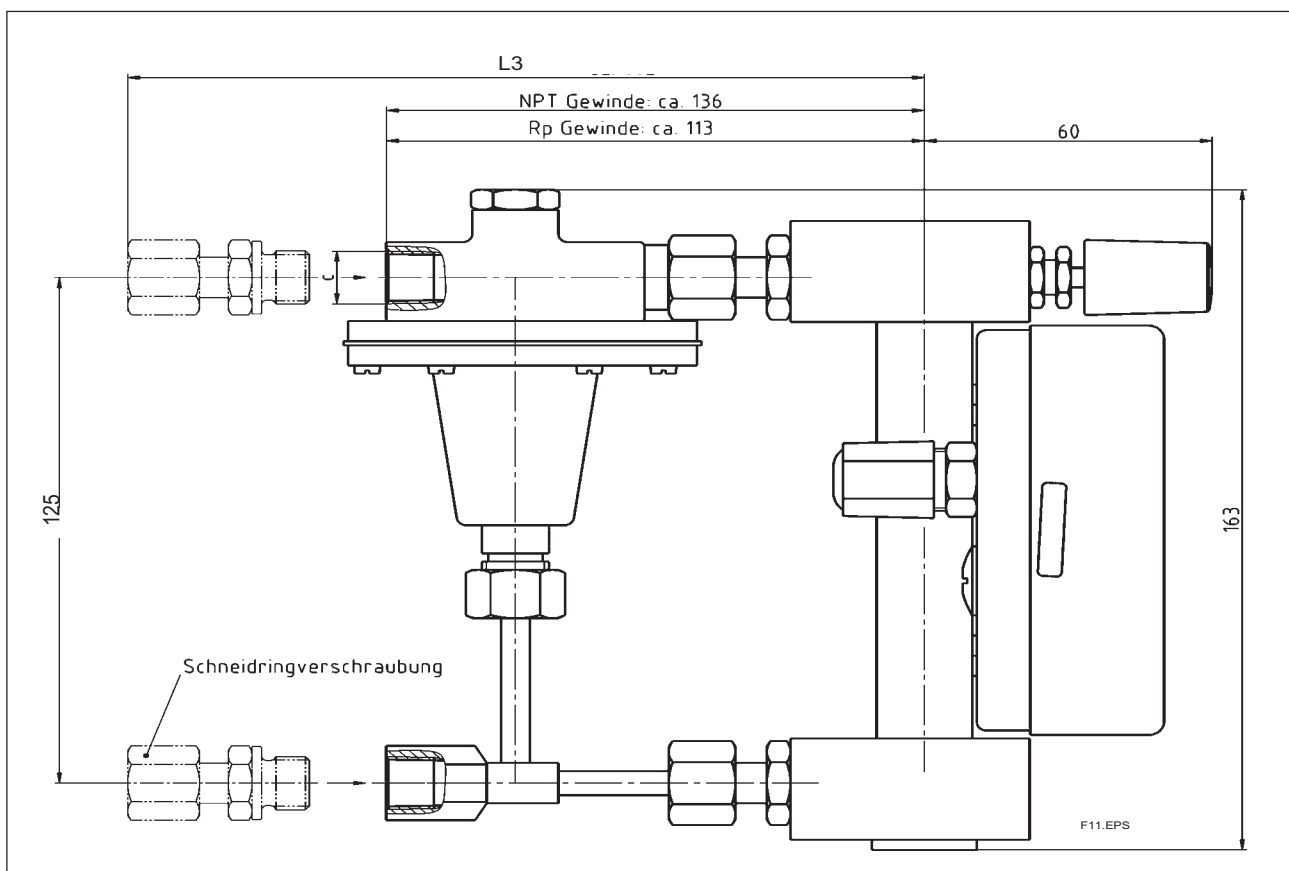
Ausführung mit Ventil im Ausgang und Gegendruckregler
